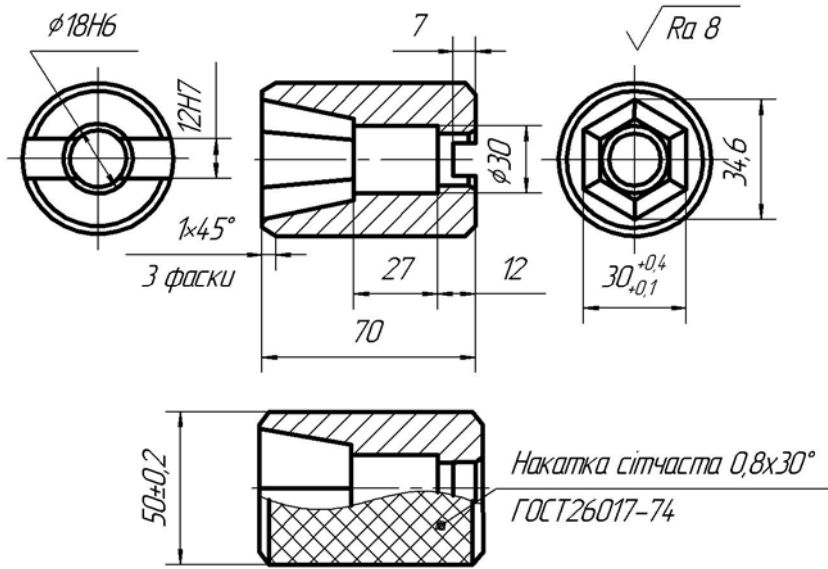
Приклад креслення деталі, форма й розміри якої виявляються двома видами та двома розрізами
